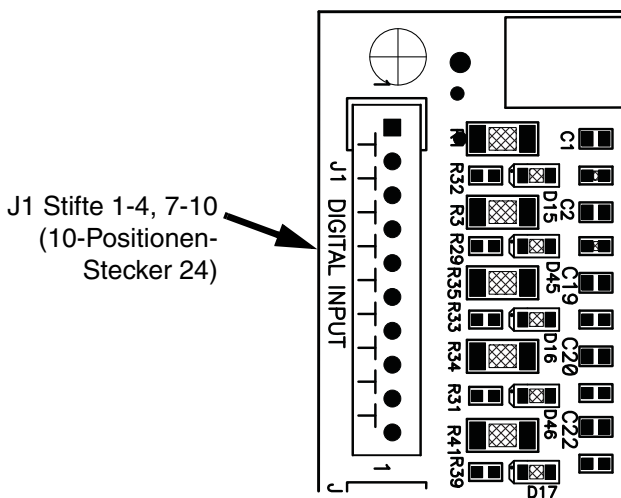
RoboMix Stecker der J1-Steuerkarte
